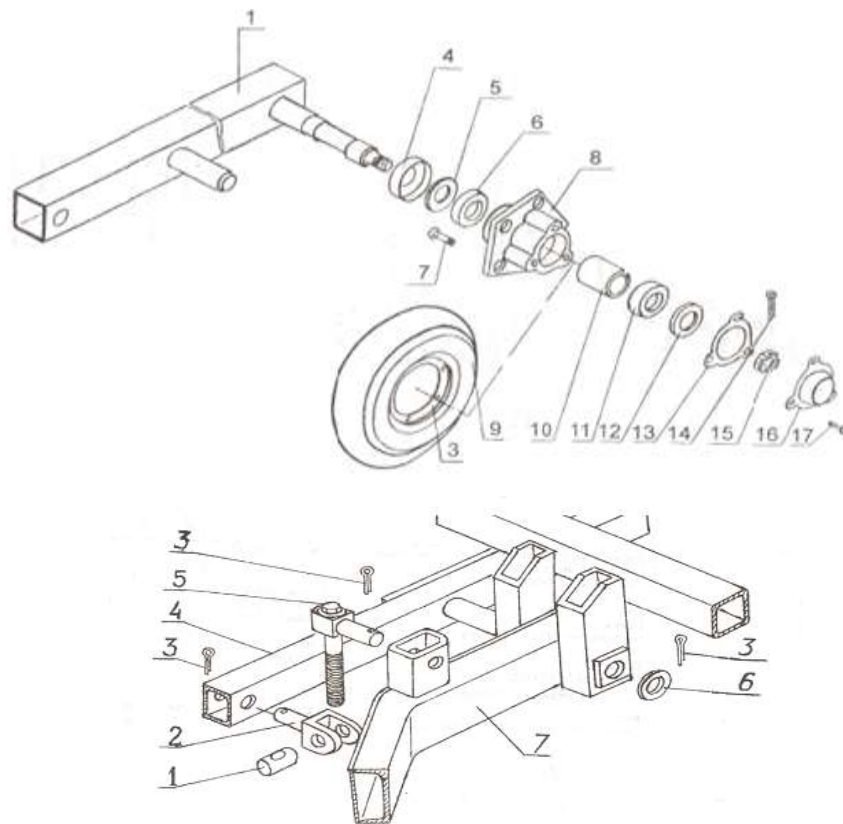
Конструкція ходової частини культиватора КПС-4.
